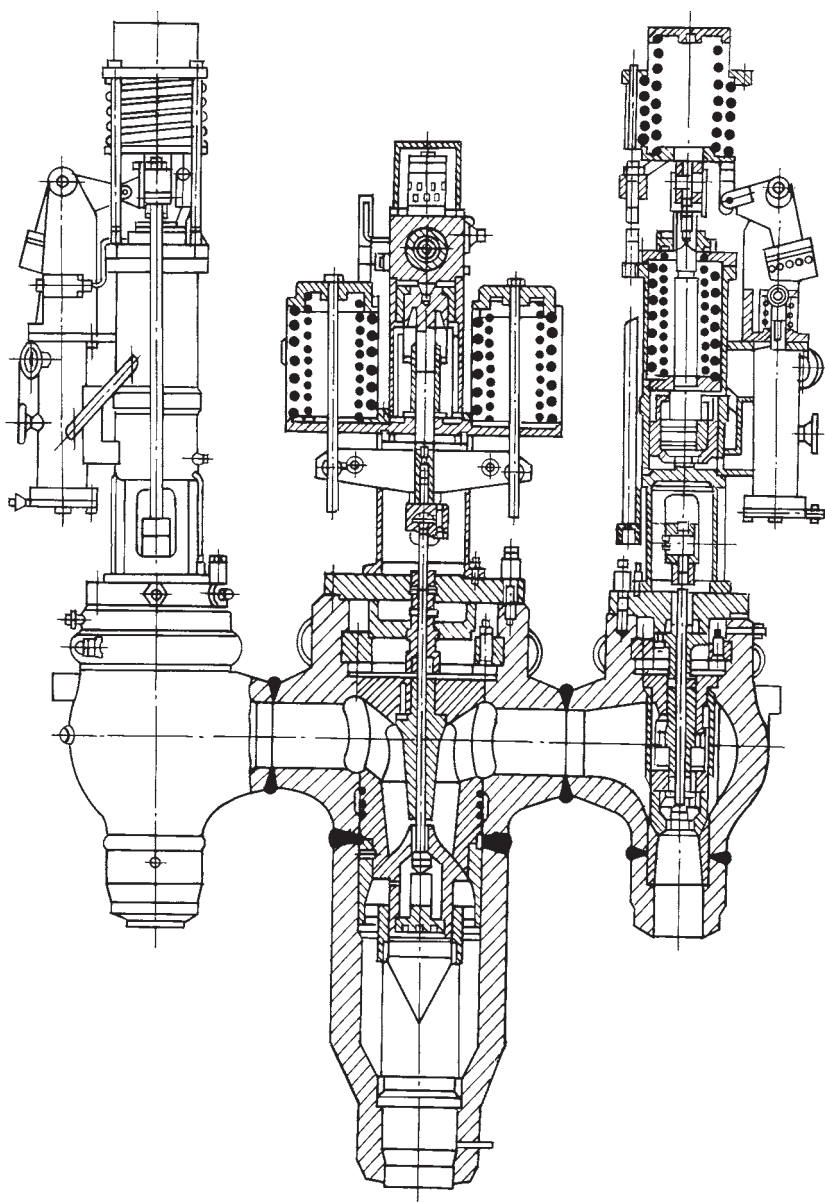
Блок стопорного и регулирующих клапанов ЦВД
